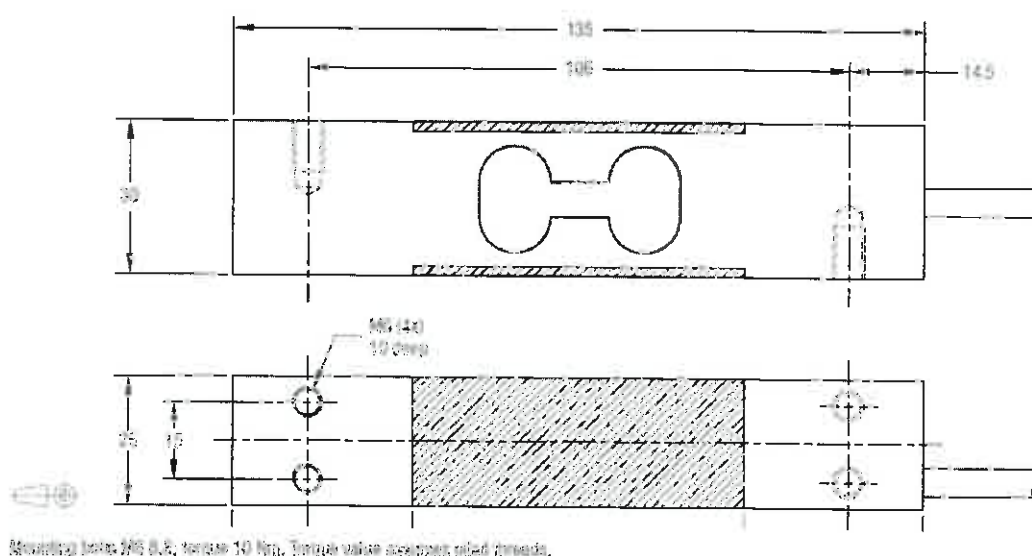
Abmessungen der Wägezelle Typ / Figure 2: Dimensions of the load cell type
